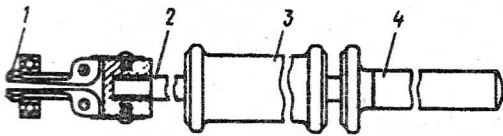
Съемник 7823-6090 для выпрессовки подшипника из коленчатого вала:
